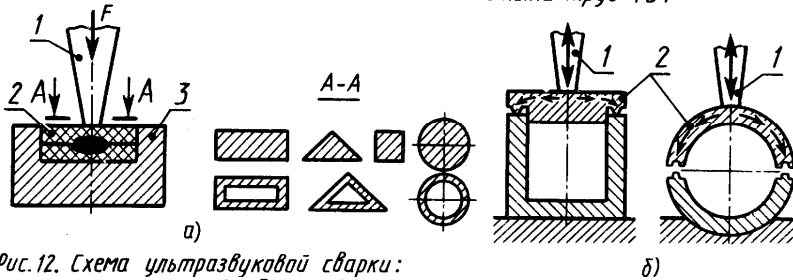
Схема ультразвуковой сварки: а - контактной; б - передаточной
